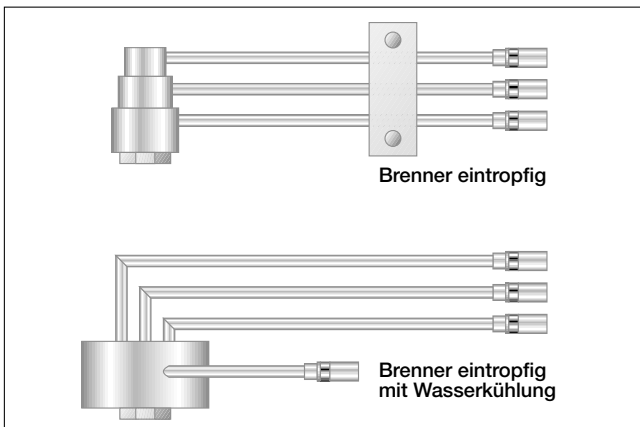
Aufbauprinzip Carboflam®-Brenner eintropfig
